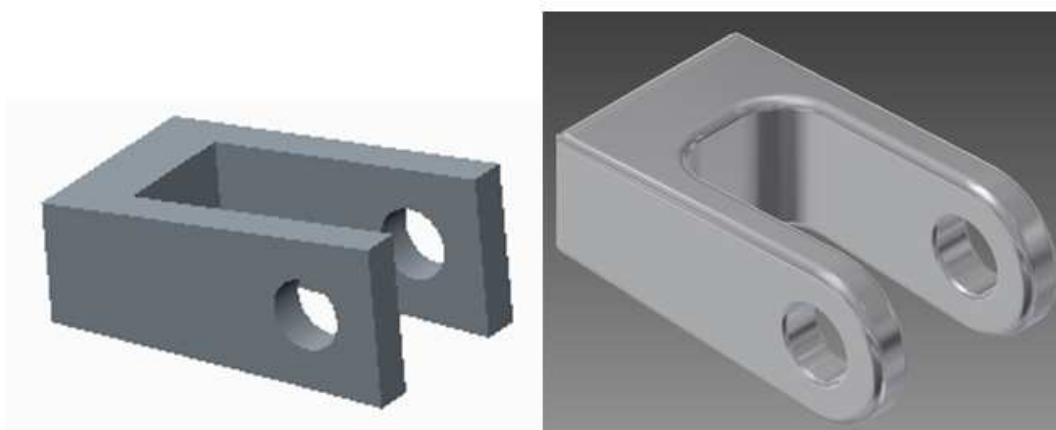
Primer diseño y diseño final de la horquilla.
